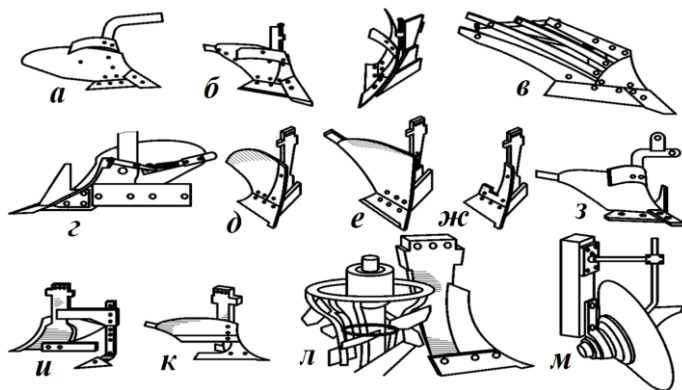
Разновидности лемешно-отвальных поверхностей корпуса плуга:
